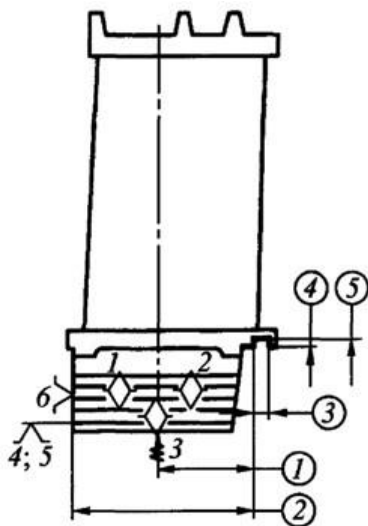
схема базування лопатки під час обробки канавки під фіксатором.
